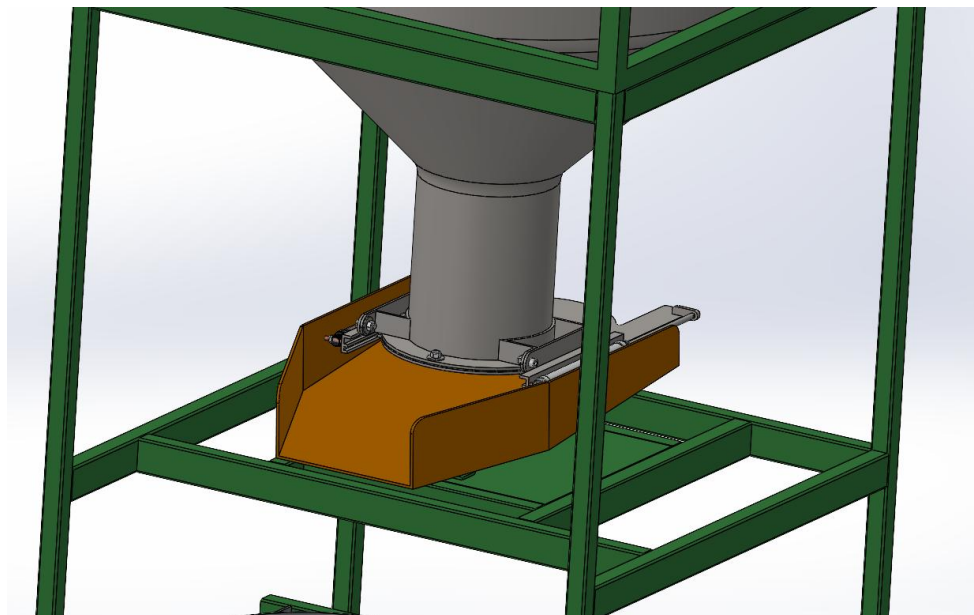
Зовнішній вигляд направляючої для зсипання
